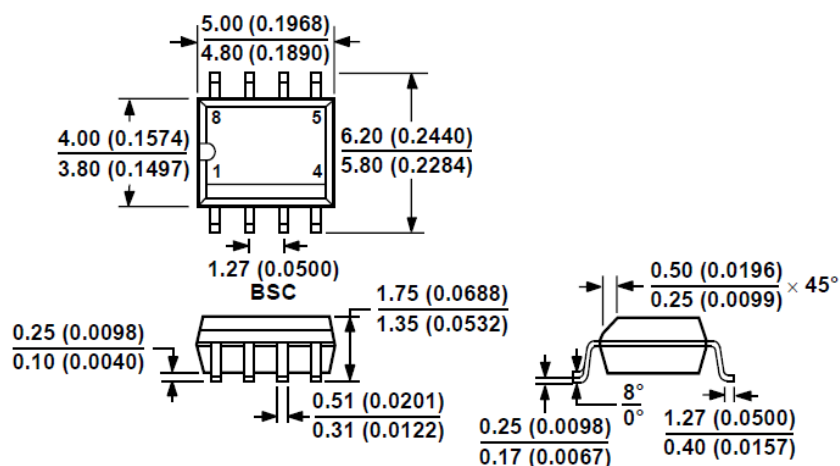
Зовнішній вигляд та габаритні розміри диференційного підсилювача AD1830ARZ в корпусі SOIC-8
